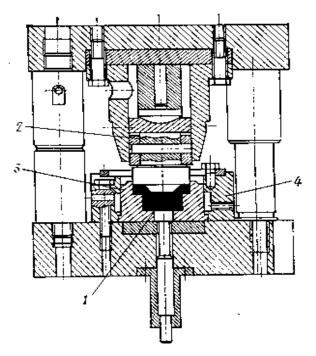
Схема штампа для жидкой штамповки поковок с фланцем: 1 — пуансон сменный; 2 — пуансон сменный; 3 — матрица; 4 — обойма с каналами для водяного охлаждения матрицы
